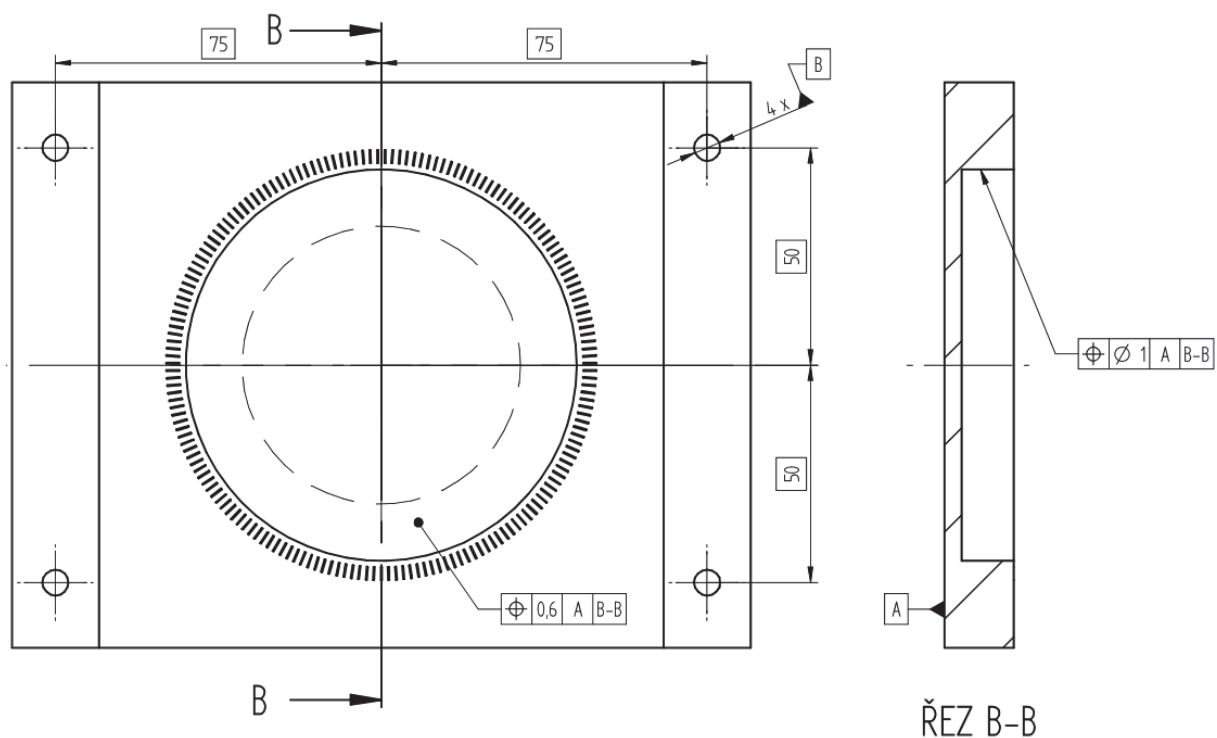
Rozměrové tolerance pro součást "otočný stůl"
